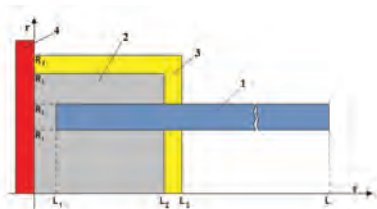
Расчетная схема подогрева стенки трубы: 1 – стенка трубы; 2 – сменная насадка для подогрева; 3 – слой теплоизоляции; 4 – нагревательная пластина сварочного аппарата
